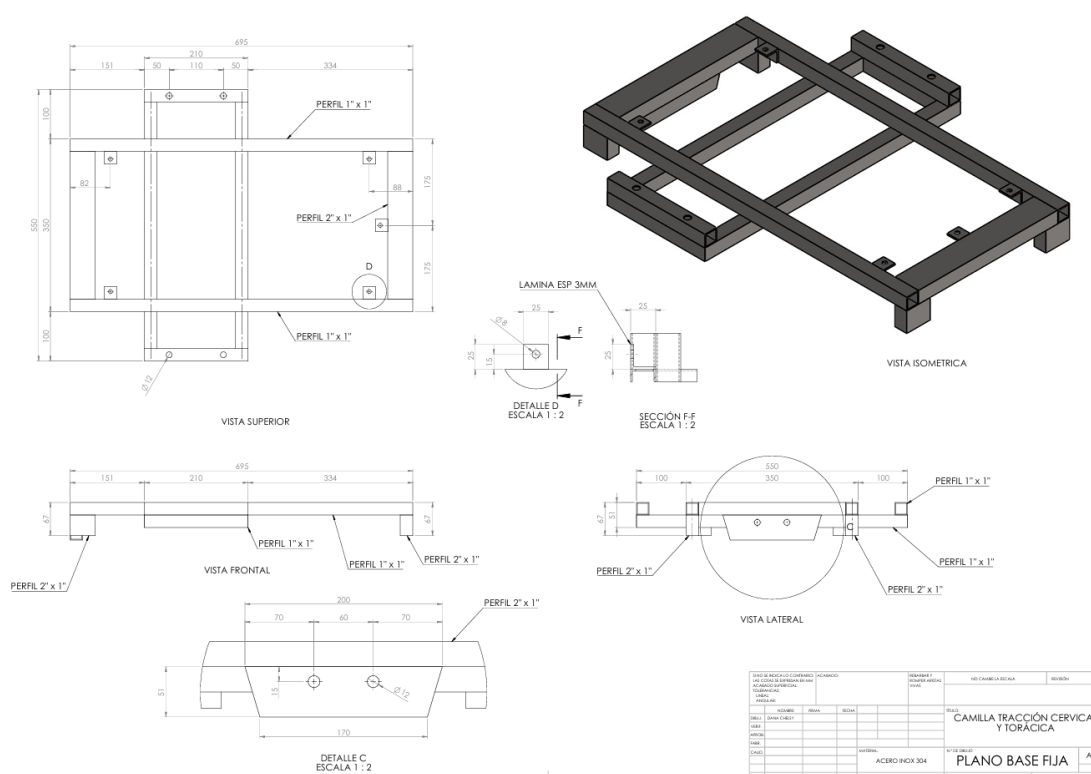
Plano de la estructura del carro fijo en el ejemplar.
